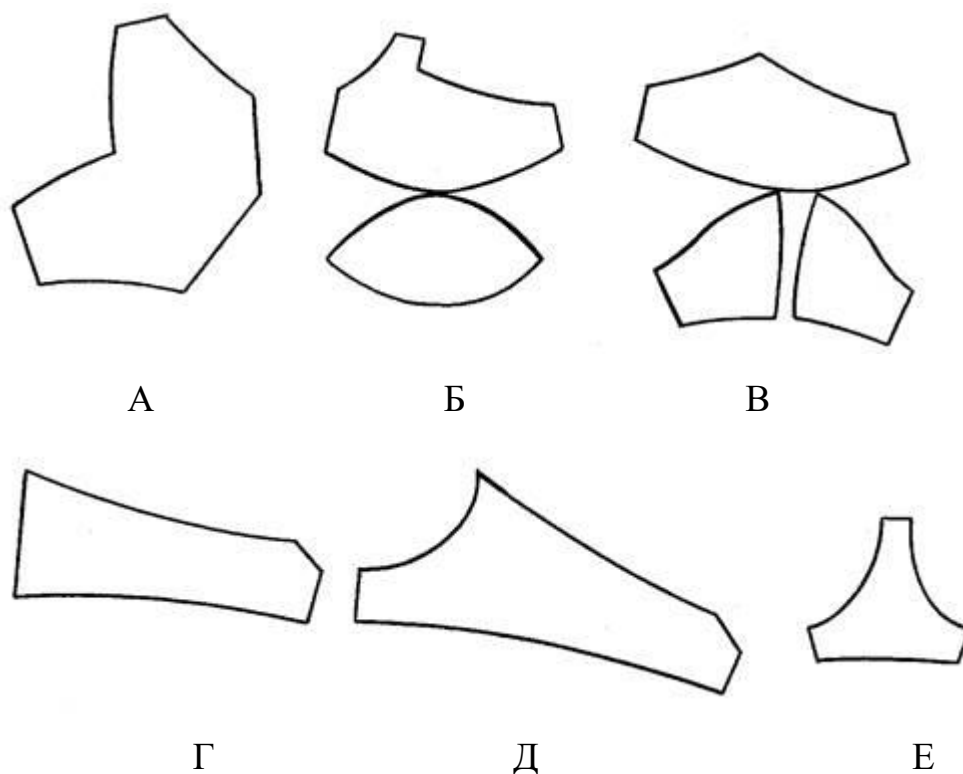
Деталі бюстгальтера: А – цілінокроєна чашка; Б – верхня та нижня деталі чашки овальної форми; В – верхня та нижні деталі чашки квадратної форми; Г – бічна деталь поясу для бюстгальтера із квадратною формою чашок; Д – бічна деталь поясу для бюстгальтера з овальною формою чашок; Е – передня деталь поясу
